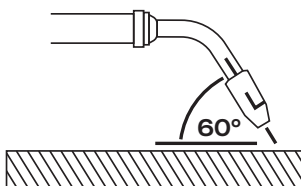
Положение сопла горелки при сварке, угол А
